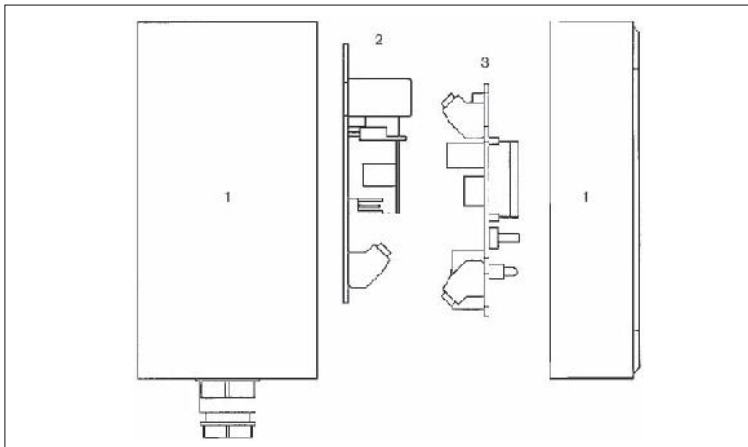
Ersatzteile für Redox-Transmitter 8206 Wandmontage-Ausführung
